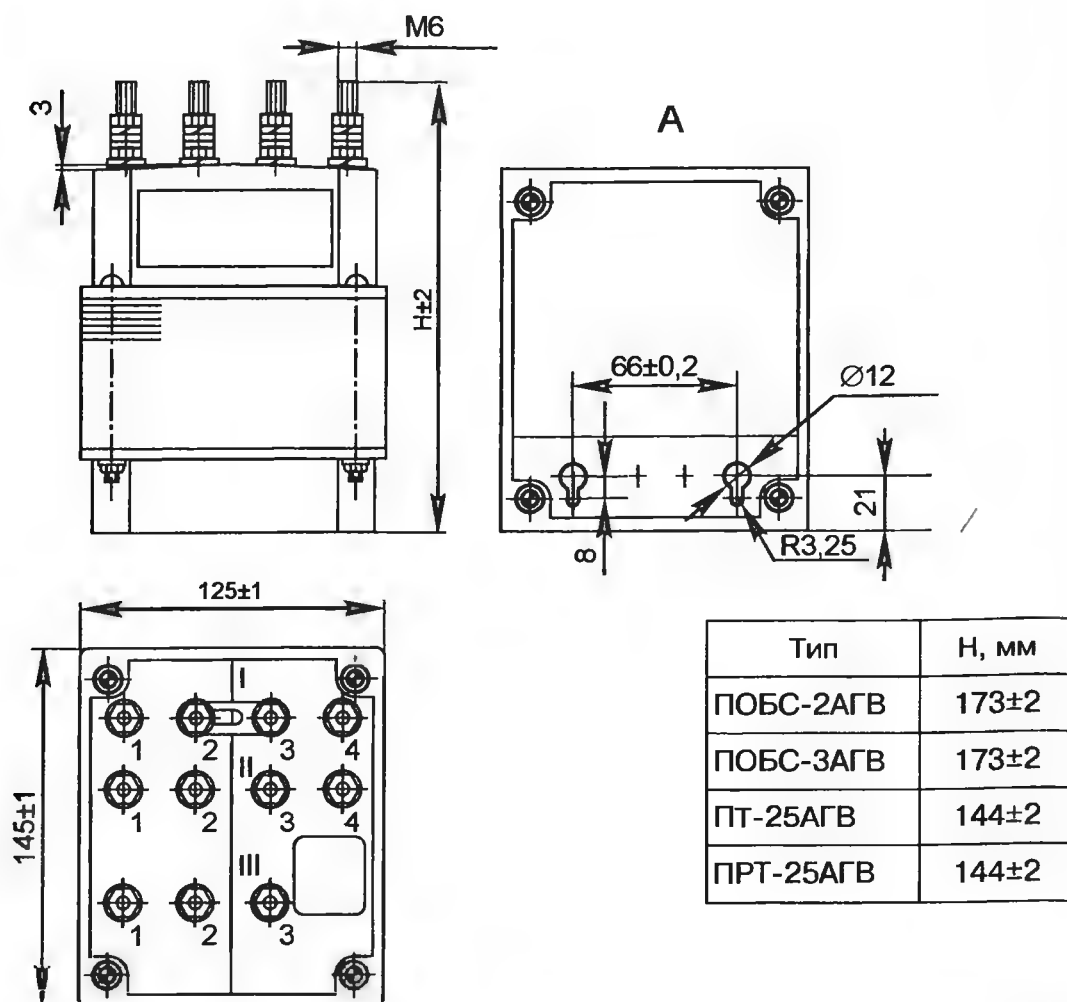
Установочные, присоединительные и габаритные размеры трансформаторов ПОБС-2АГВ, ПОБС-3АГВ, ПТ-25АГВ, ПРТ-25АГВ
